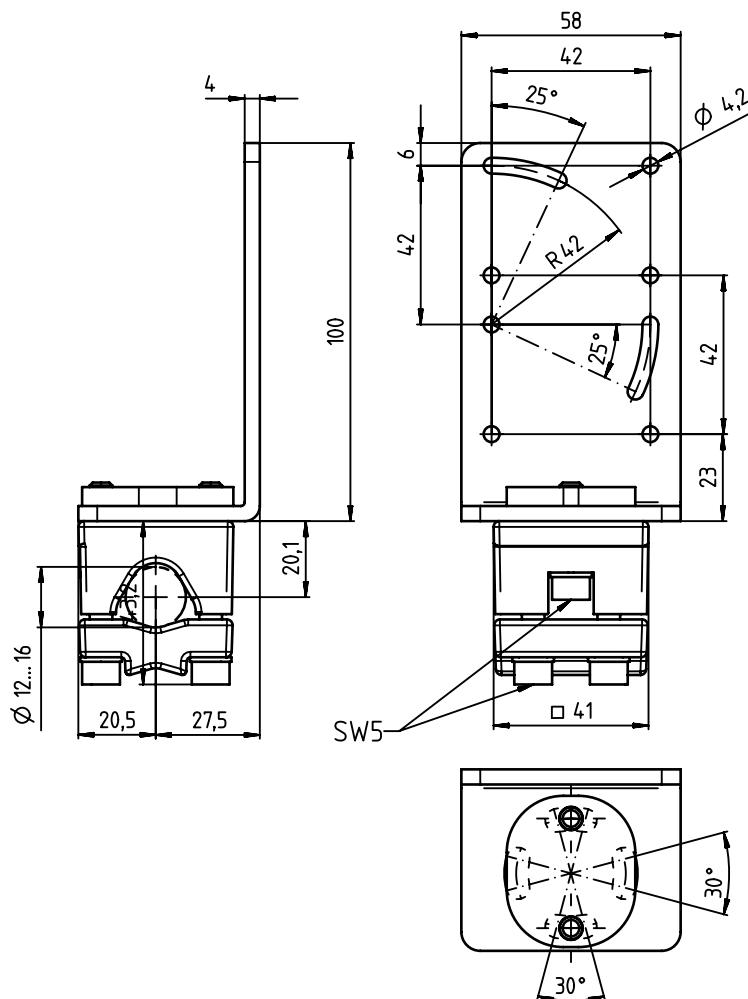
Maßzeichnung Befestigungswinkel BT 300-W
